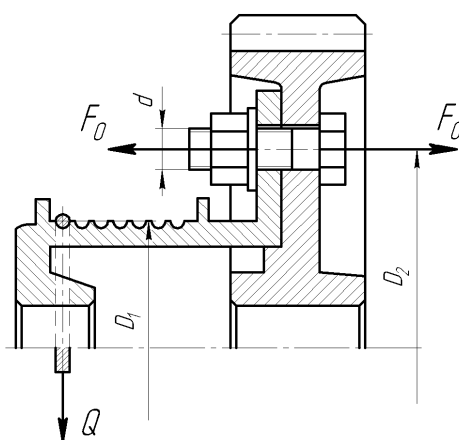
,в. Конструкція болтового з'єднання зубчастого колеса з барабаном (варіант I)
